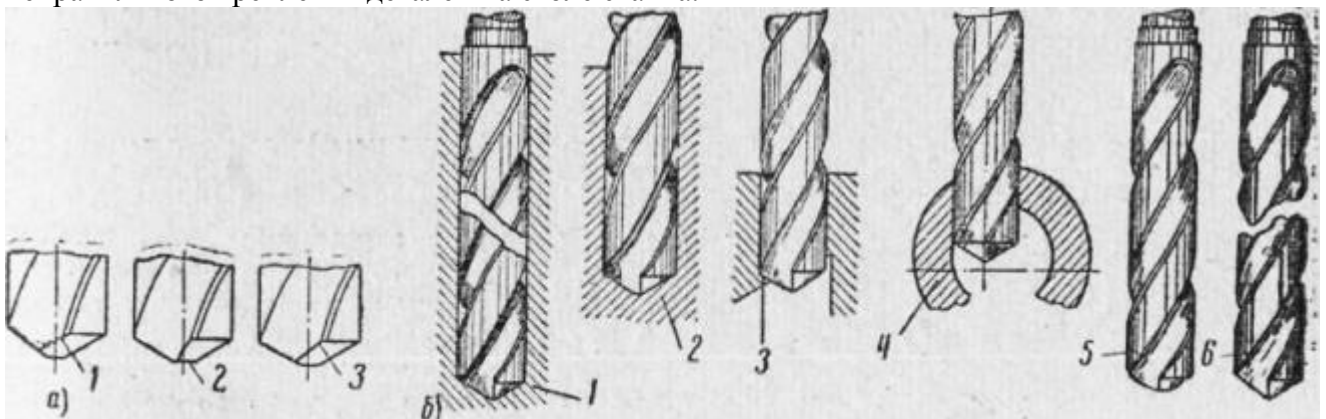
Затупление и поломка сверл: а — участки, подвергающиеся затуплению: 1 — выкрошенная режущая кромка, 2 — затупленная поперечная кромка, 3 — затупленный угол; б — примеры поломки сверл: 1 — сверло глубоко вошло в отверстие, не выходит стружка, 2 — сверло натолкнулось на постороннее твердое включение, 3 — неравномерный выход сверла из отверстия по его окружности, 4 — нецентральный выход сверла из отверстия, 5 — затупление сверла под влиянием чрезмерно большой скорости резания, 6 — поломка сверла вследствие чрезмерно большой подачи
